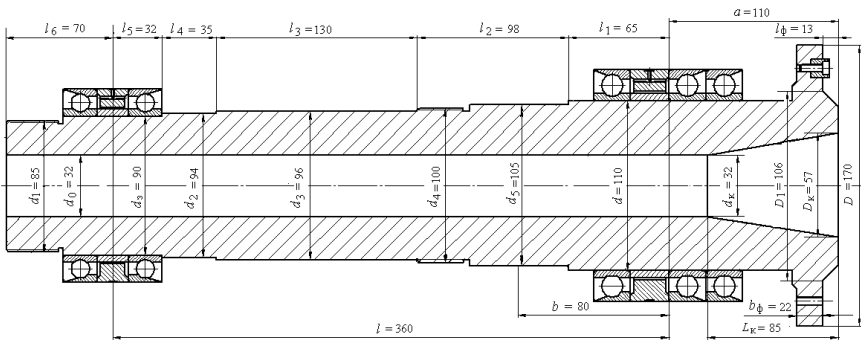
Конструктивная схема шпиндельного узла токарного станка и основные конструктивные размеры
